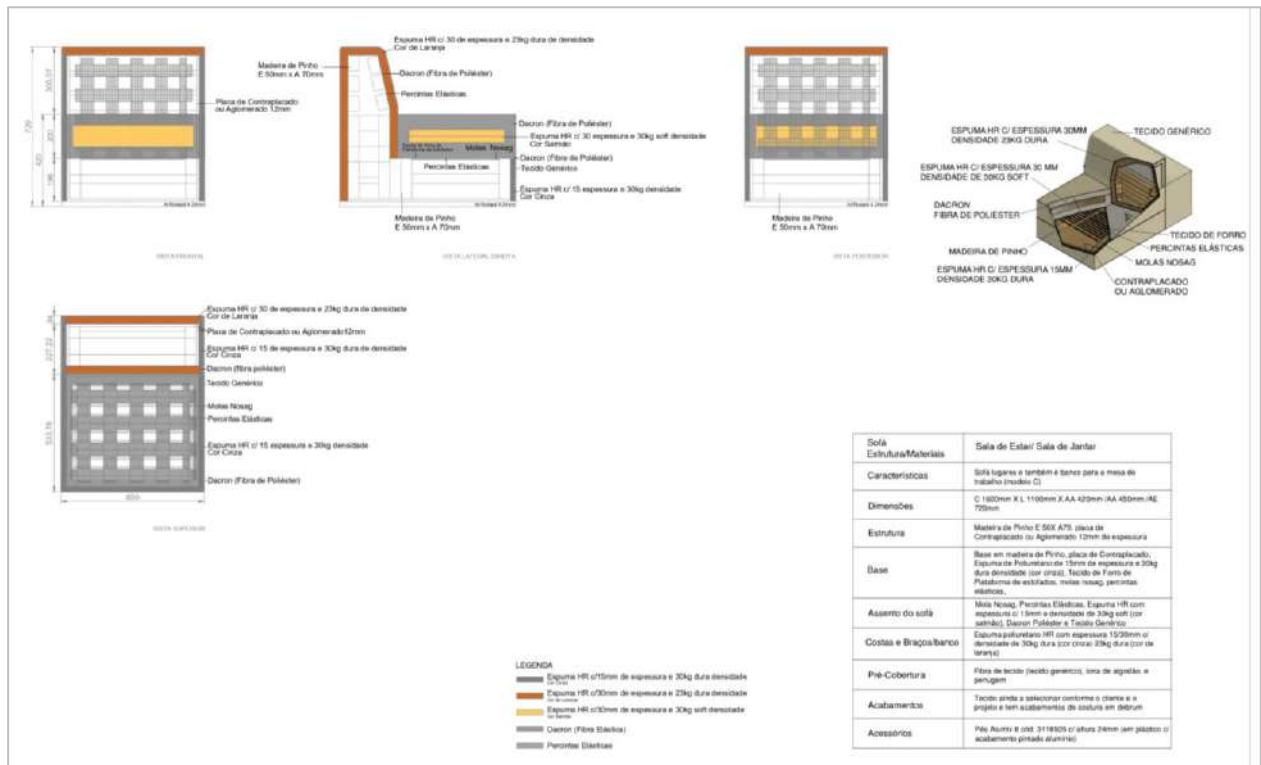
Desenhos técnicos-Cortes sofá módulo C. Fonte: Júlia Rodrigues
